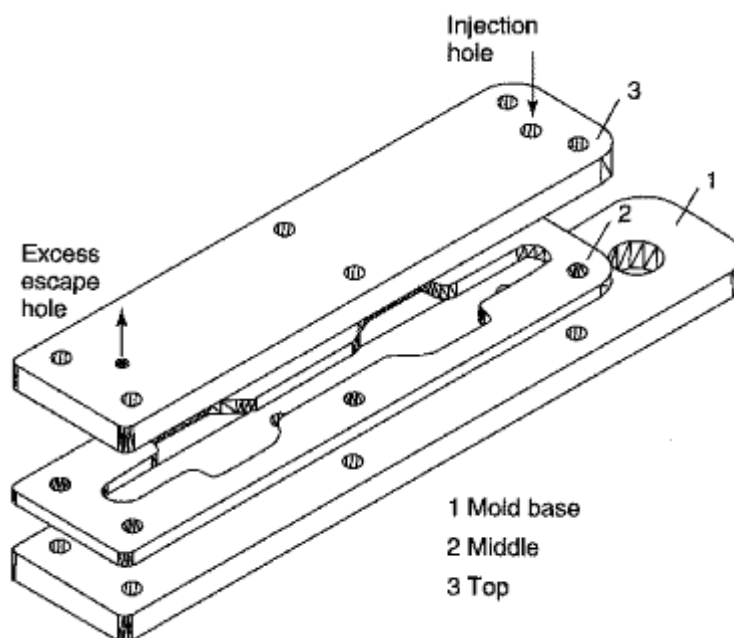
Representação esquemática de um molde utilizado para o fabrico de provetes em adesivo maciço [17]
